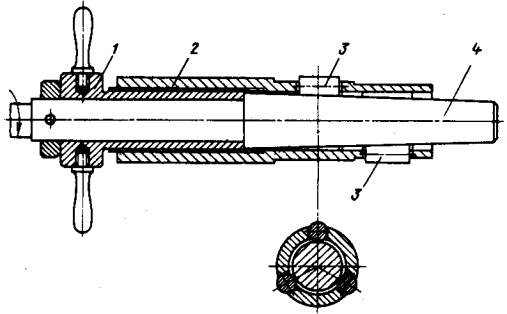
Цилиндрическая вальцовка с разжимом роликов: 1 — винт подачи; 2 — корпус; 3 — ролики; 4 — разжимающий конус
